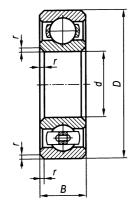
Подшипник шариковый радиальный однорядный
